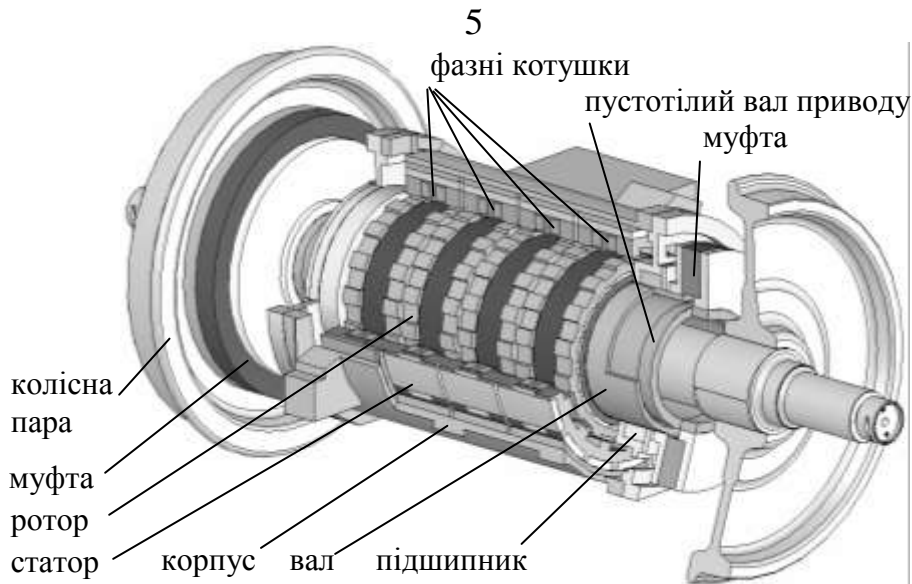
Конструкція безредукторного колісно-моторного блоку з АІД
